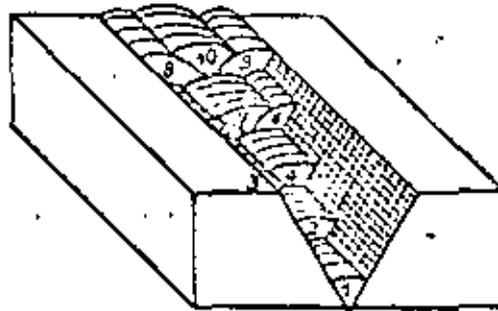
DISPOSICION DE LOS CORDONES DE SOLDADURA EN EL TIEMPO POR "PASADAS ESTRECHAS".
